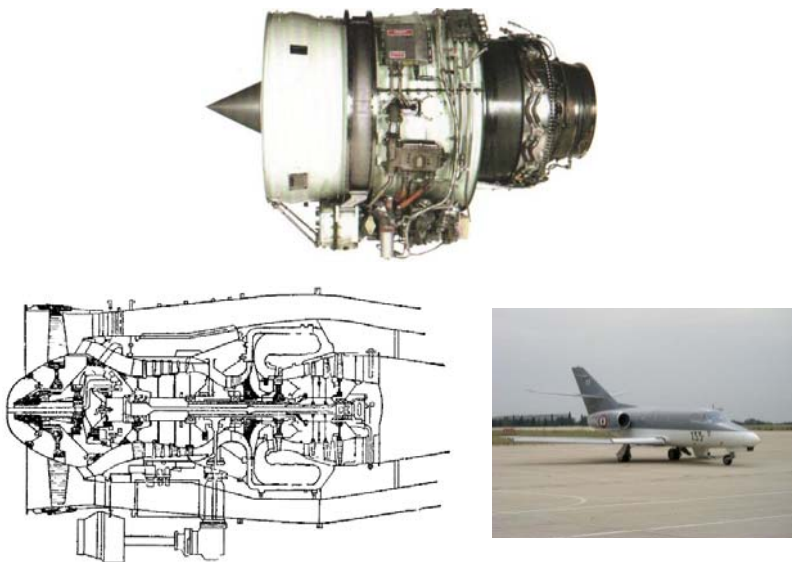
ТРДД TFE731. Внешний вид и конструктивная схема [160, 167, 172]
